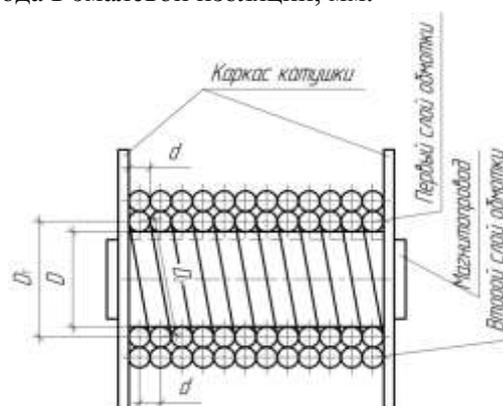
Внешний вид рассматриваемой обмотки электромагнитного устройства
